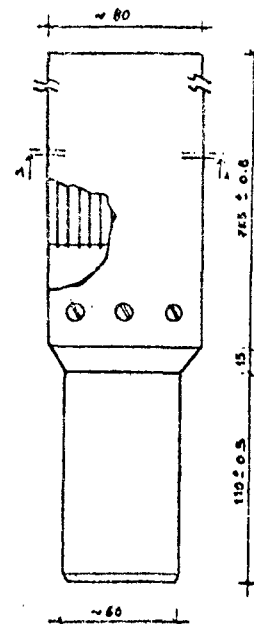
Corte vista lateral izquierdo del elemento combustible (en mm).
